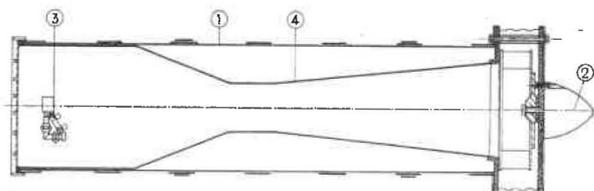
Vue en coupe du dépoussiéreur léger Samia type DV3.
